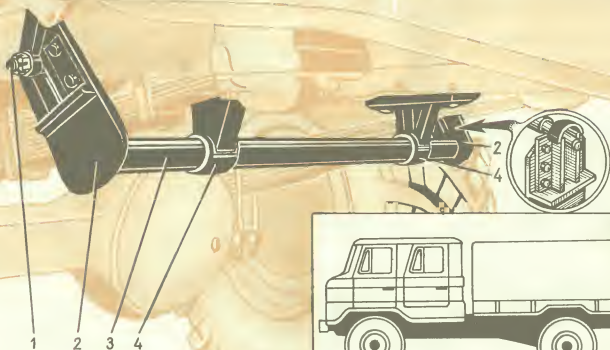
Кауассийский вариант двойного рулевого управления: 1 — палец сошки дополнительного рулевого механизма; 2 — иулисы; 3 — вал; 4 — опоры.
